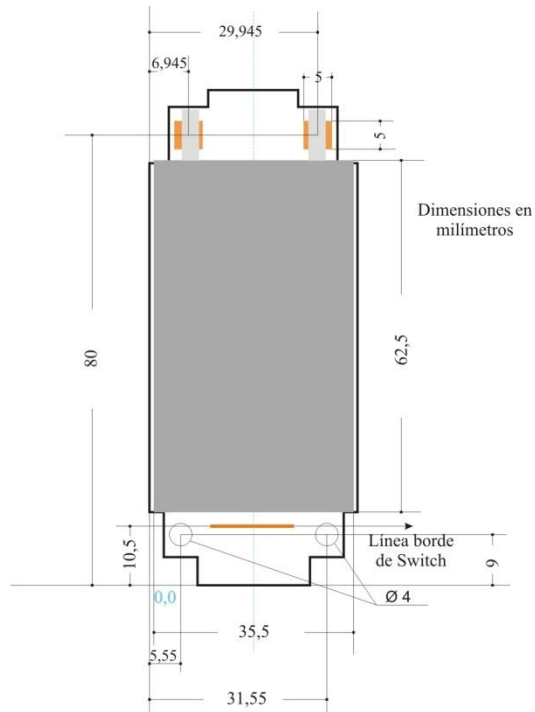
Pads para soldadura de pieza de enganche de batería, dimensiones, posición y coordenadas
